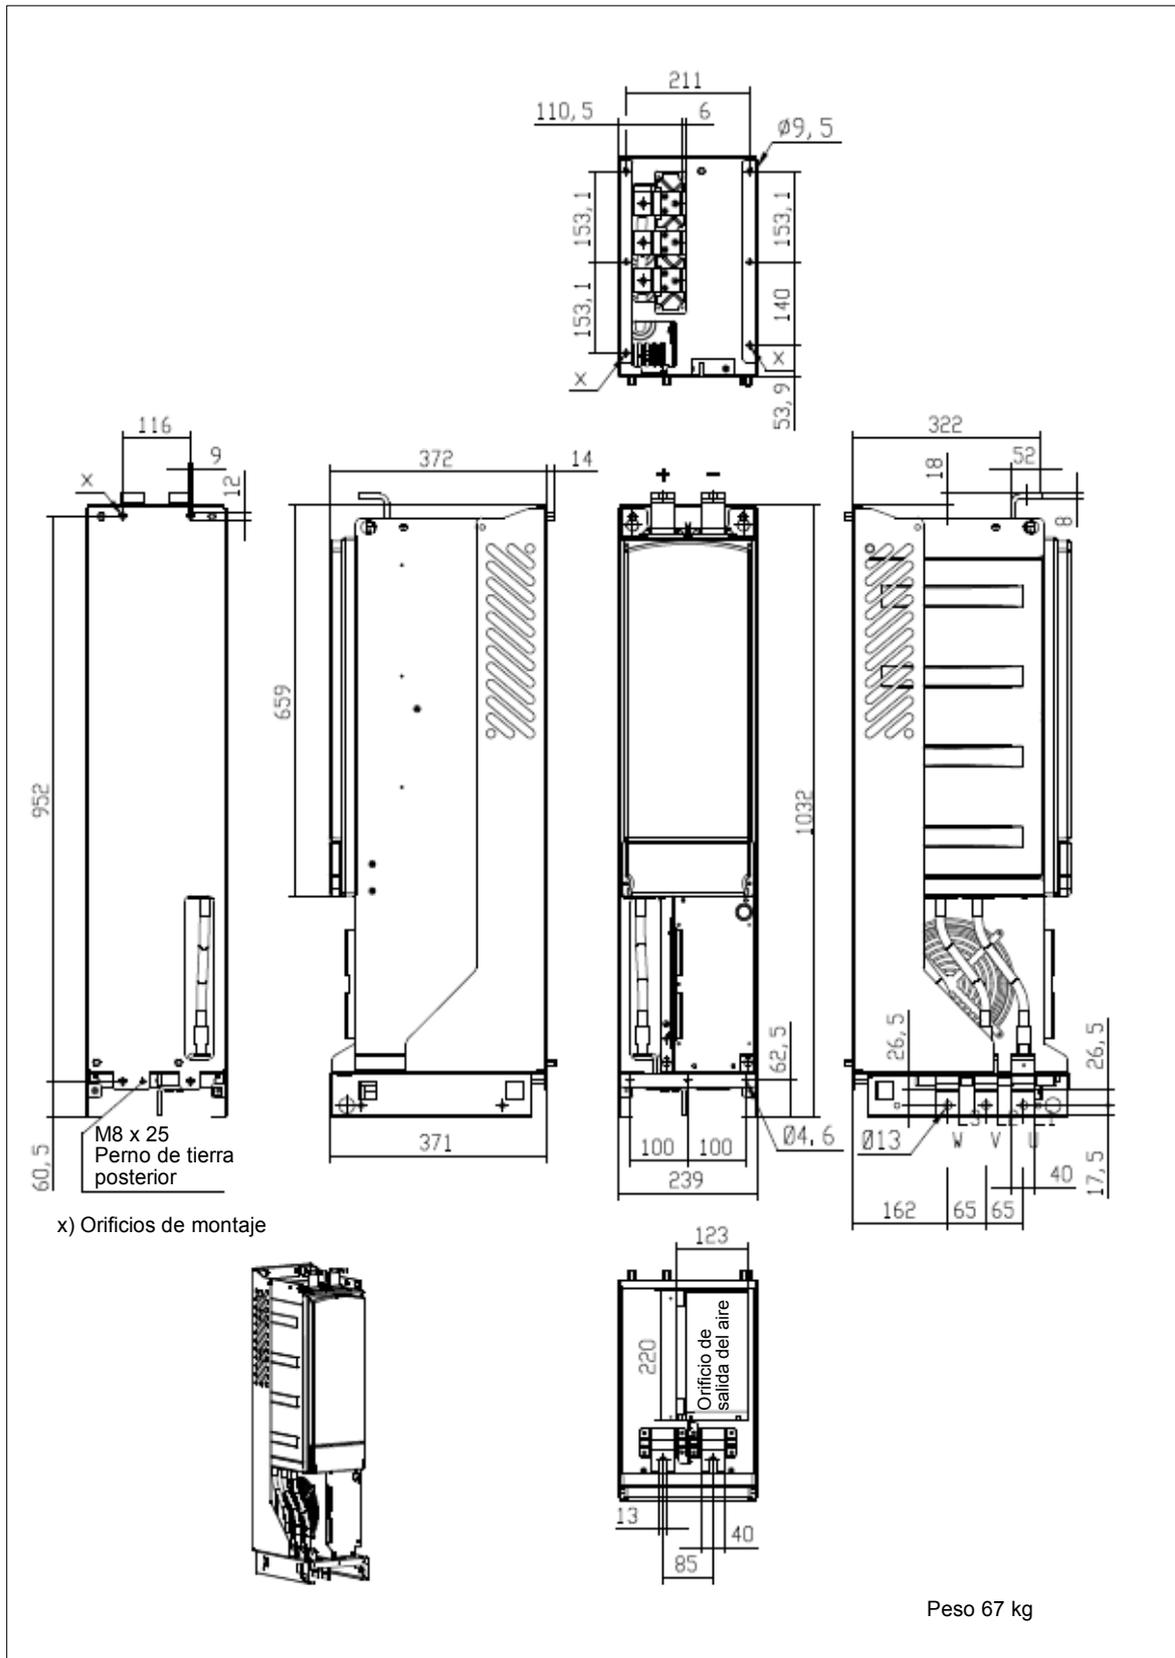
Dimensiones del inversor Vacon NXI FI9
